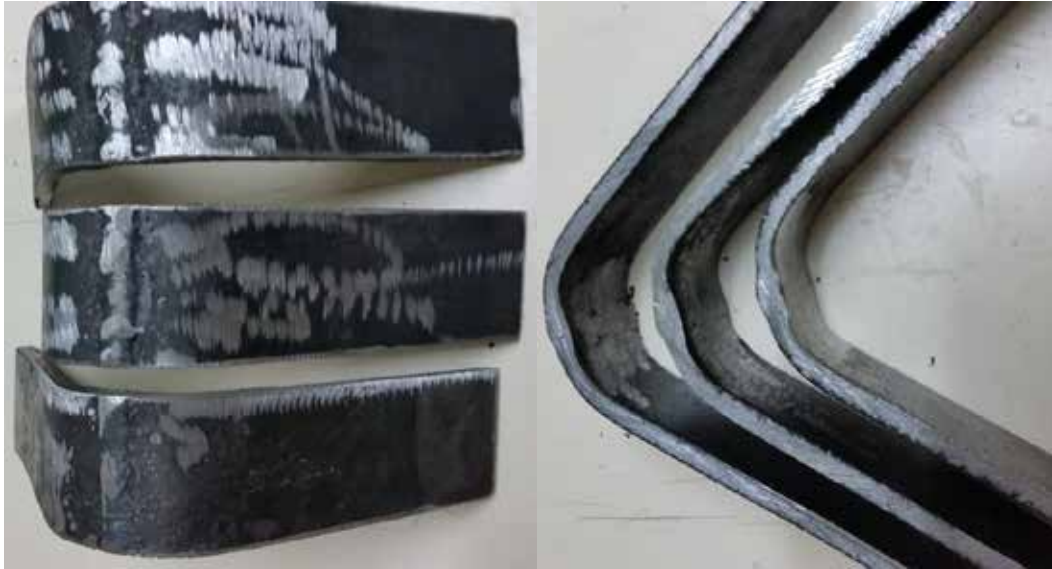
Doblado de la probeta soldada con electrodo E-6013 a 80Amp.
